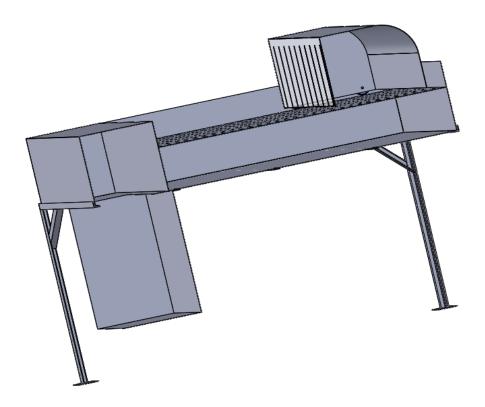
7: Vue de coupe de la machine sur SolidWorks
